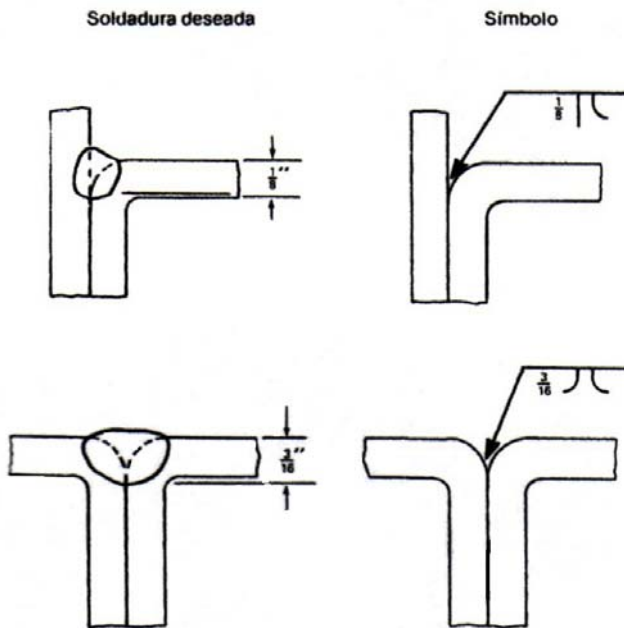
Símbolos de soldadura en los que se especifica el tamaño de las soldaduras de ranura con acampanado.
